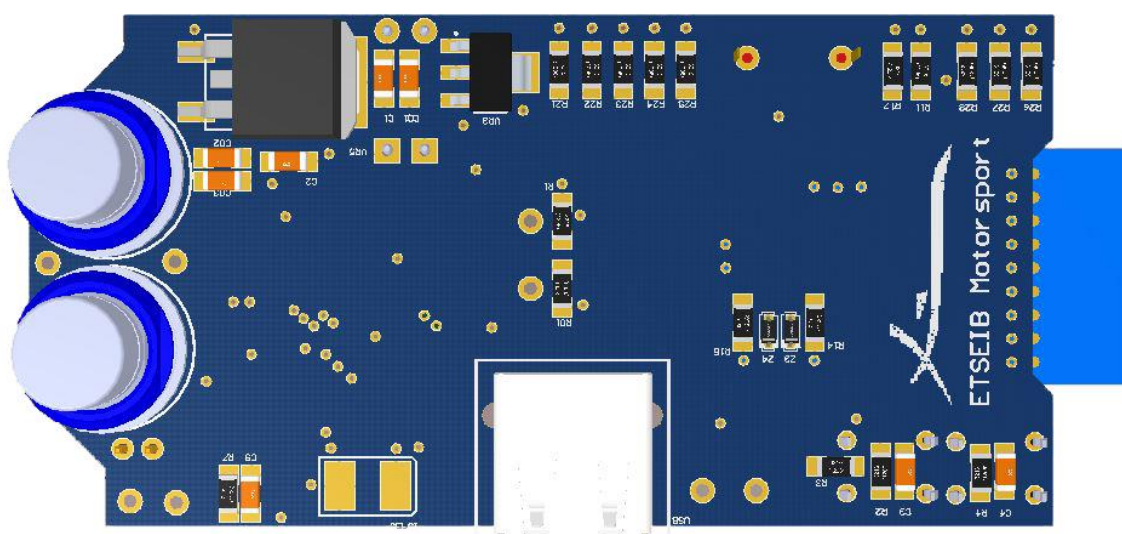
Representació en 3D de la part frontal de la PCB. Font: pròpia.
